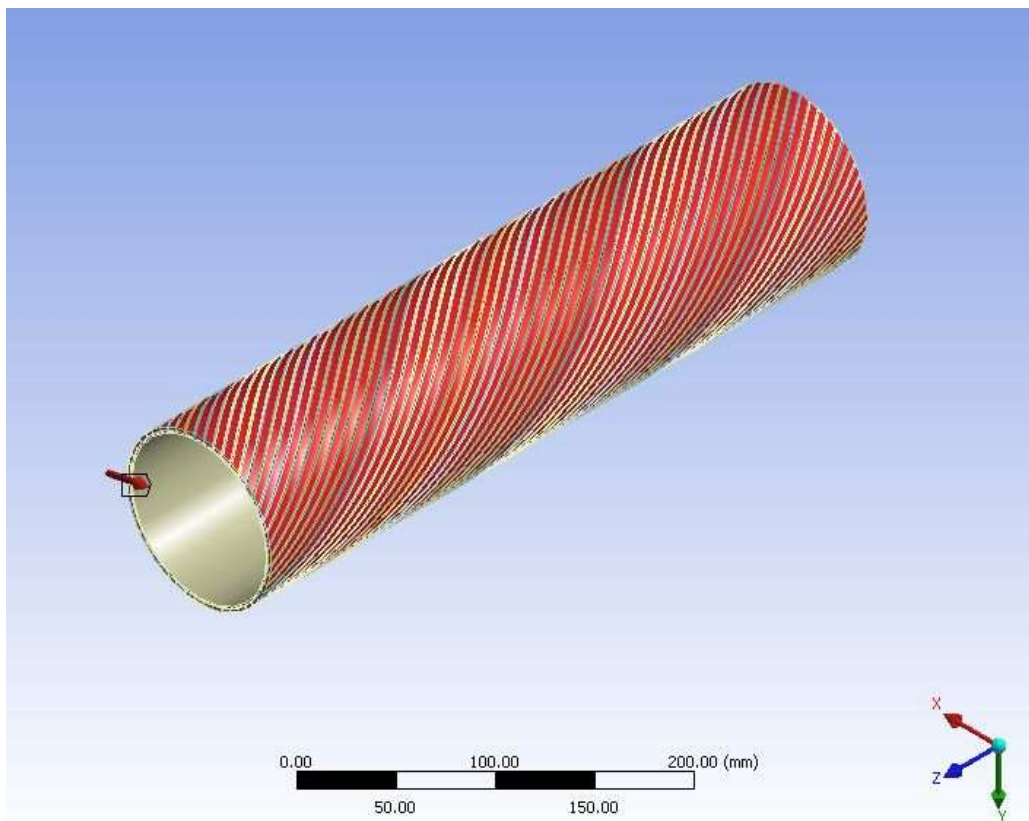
Modelo da armadura interna com aplicação da pressão externa.
